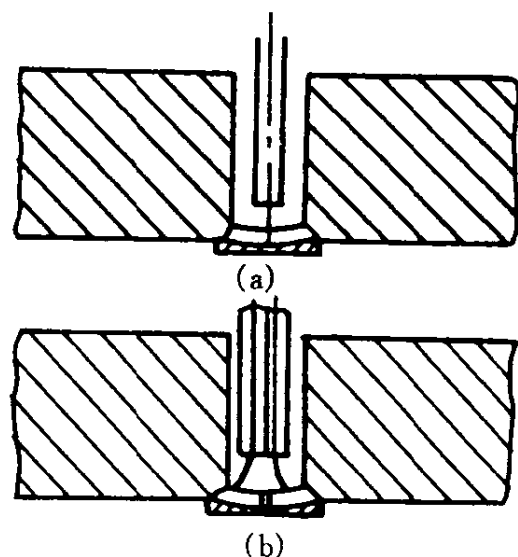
单丝或双丝窄间隙 MIG 焊
